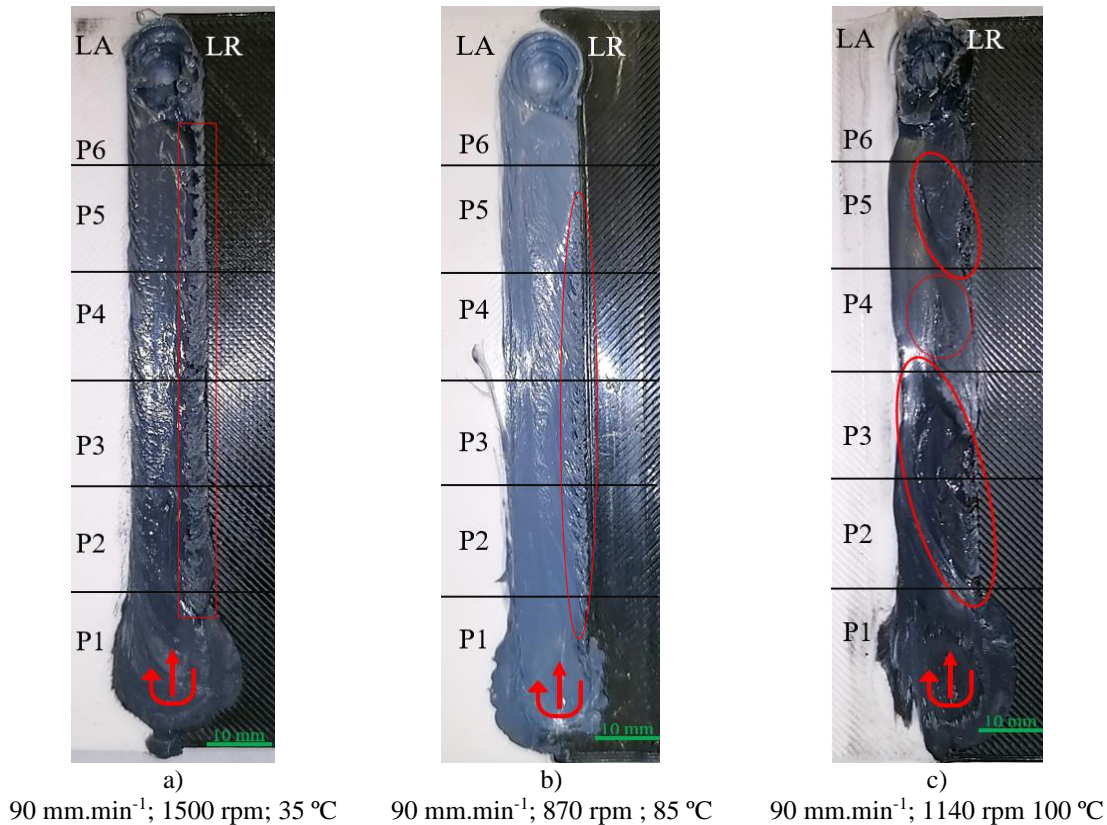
Fratura soldadura 3D\_PLA\_3.
